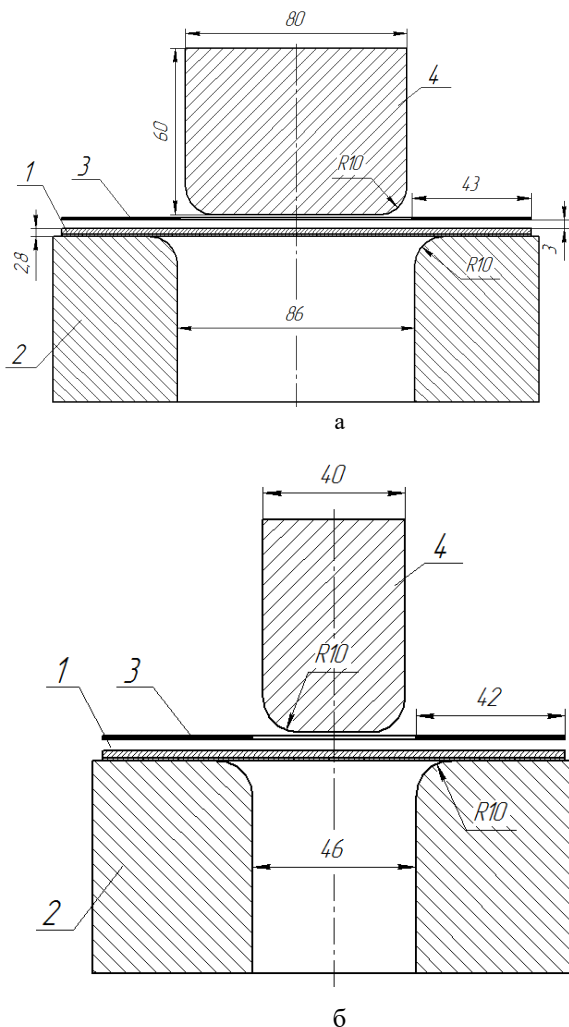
Фізична модель розположення заготовок і інструмента: а – фронтальний вид, б – профільний вид.
